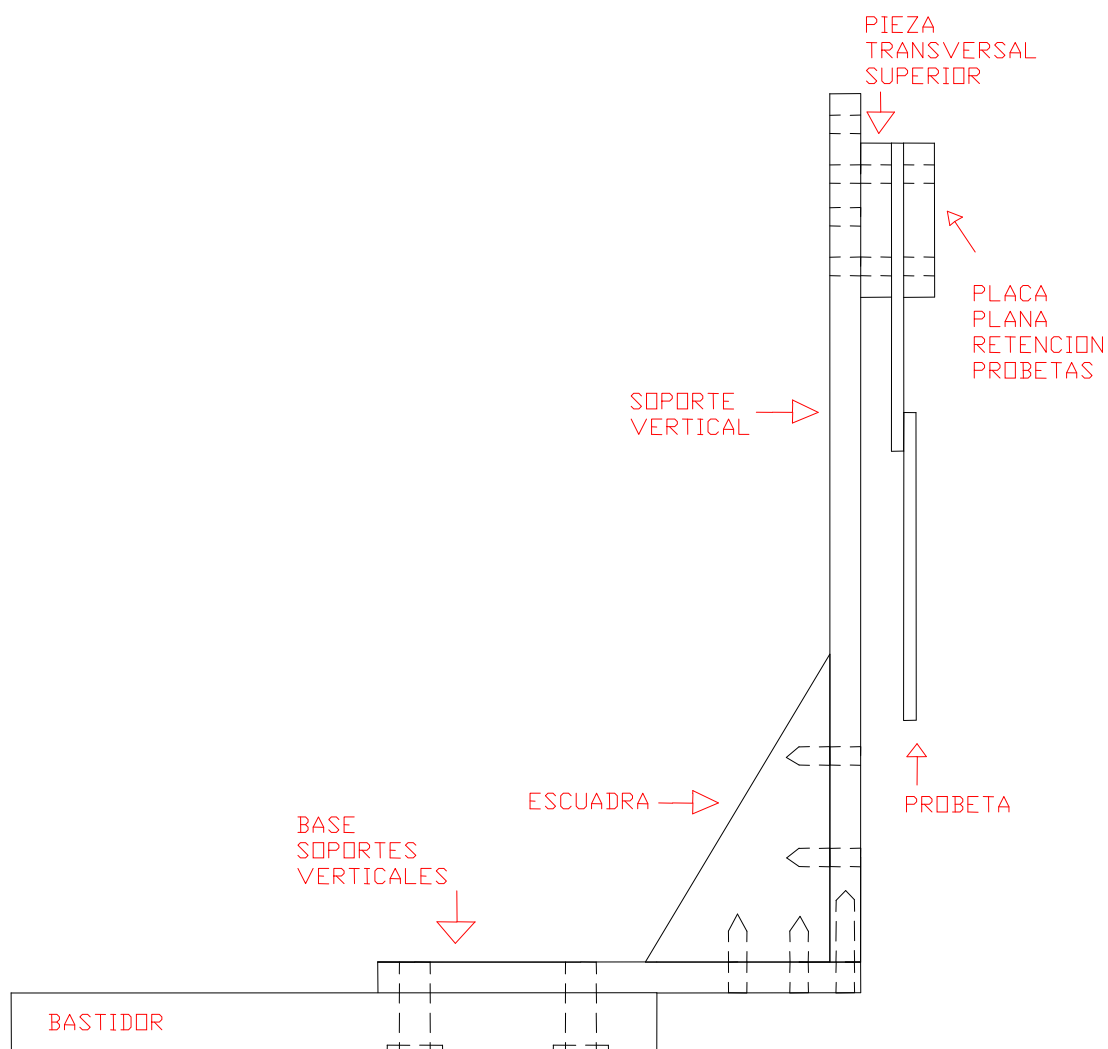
Vista lateral conjunto sin guía ni soporte móvil.
